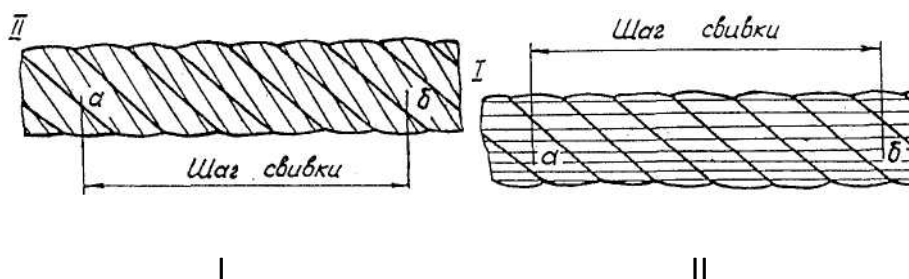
Измерение шага свивки каната: I - крестовой свивки; II - односторонней свивки
